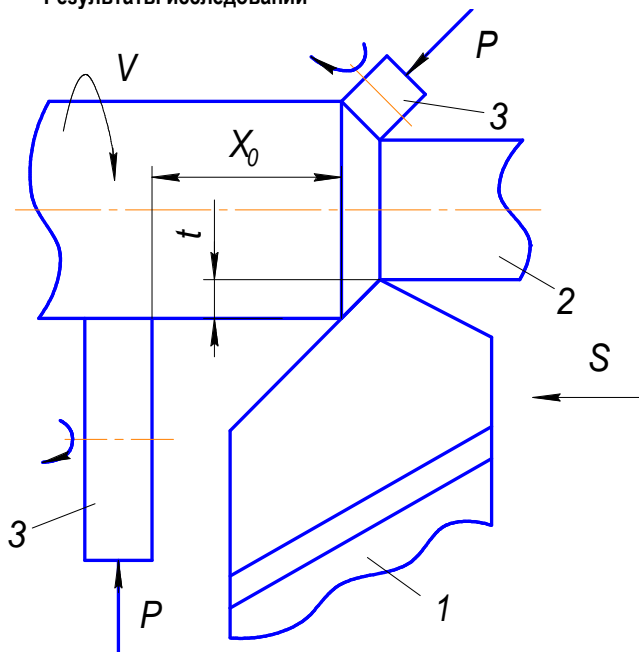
Схема обработки резанием с опережающим пластическим деформированием: 1 - резец; 2 - обрабатываемая заготовка; 3 - ролик
